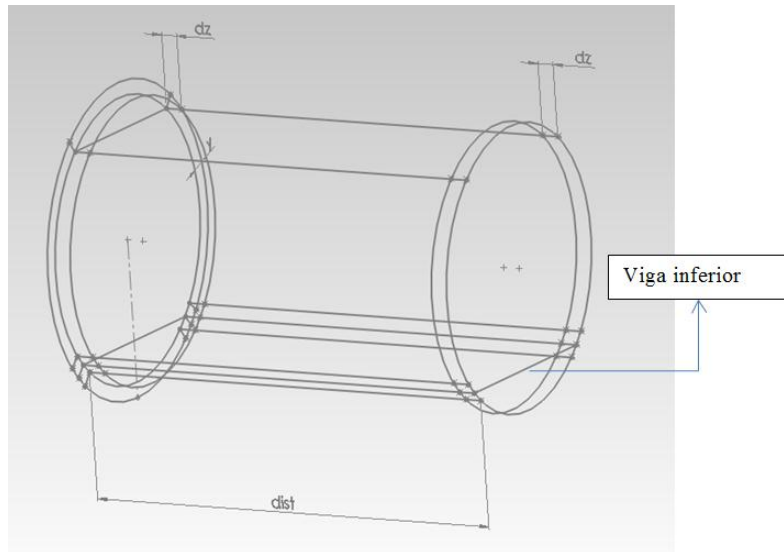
Secção lateral do modelo de construção da estrutura tubular.
